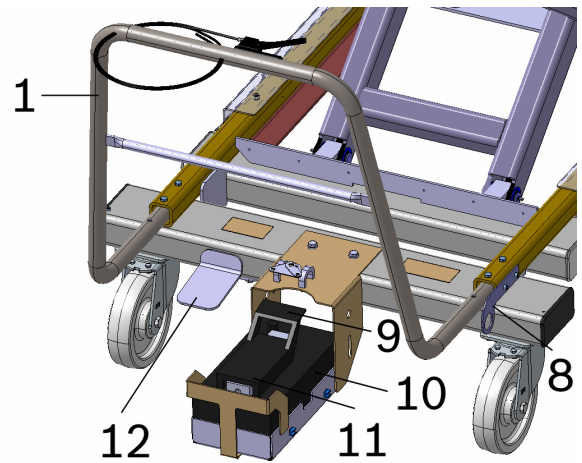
Collegamento del tubo flessibile dell'aria compressa al piano elevatore a pantografo
